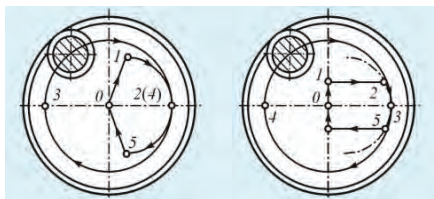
Схема фрезерования резьбы в предварительно выполненном отверстии на станке с ЧПУ:
